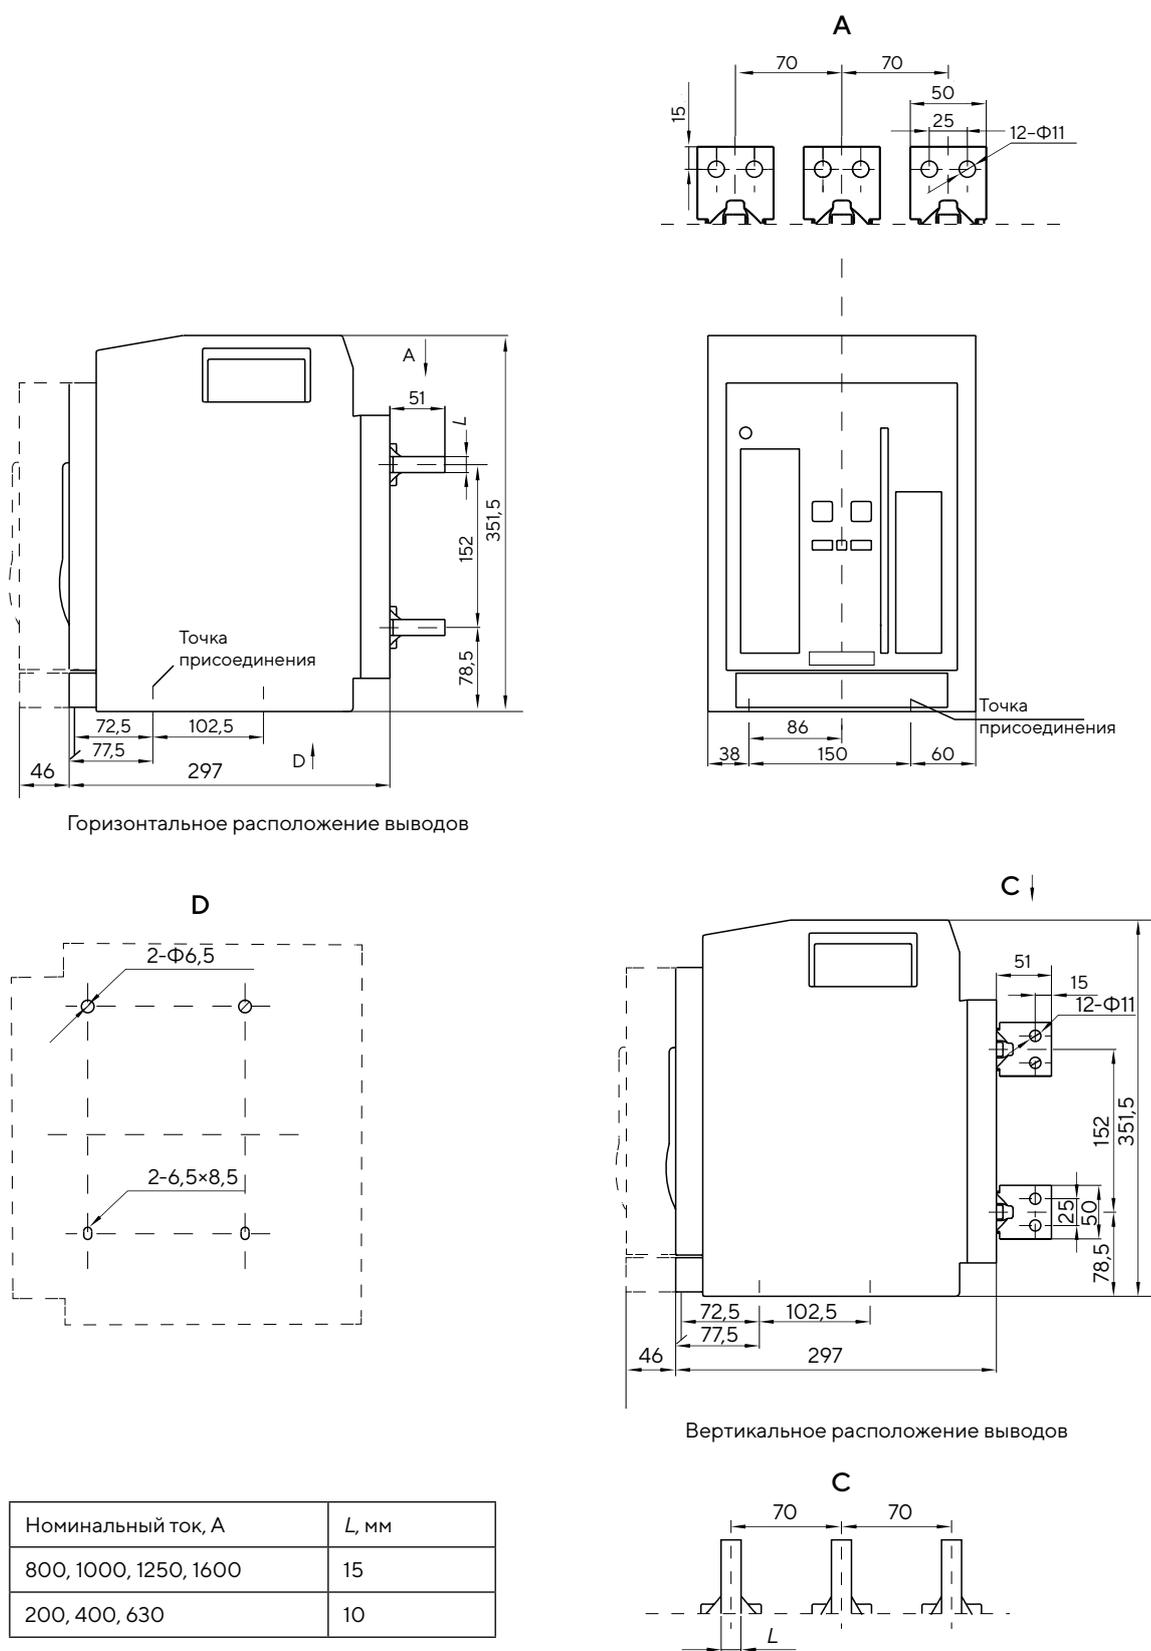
Габаритные размеры выдвижных трехполюсных выключателей типоразмера А
